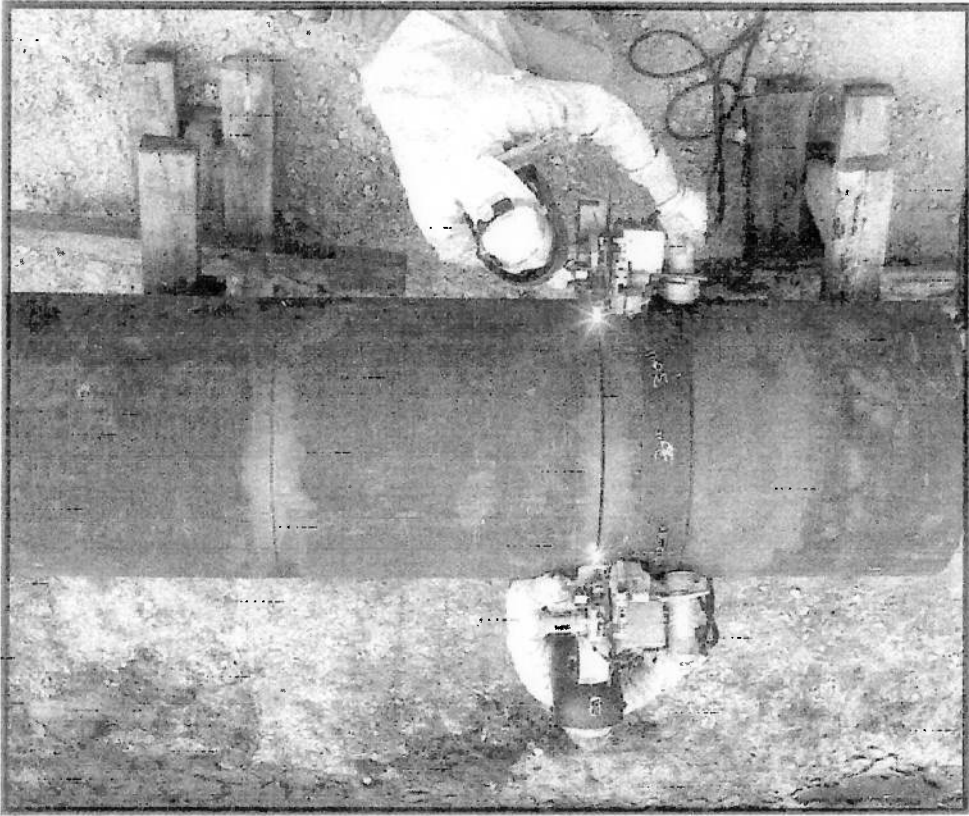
Sistema interno de Soldagem MAC com 4 cabeças, [63].
